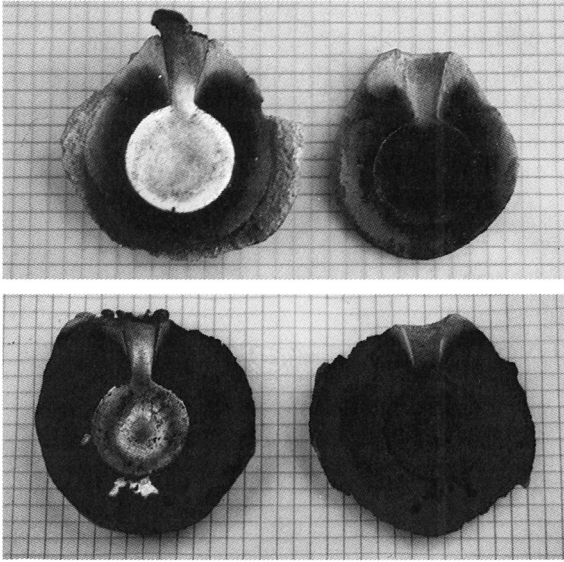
Formens reducerende indre beskytter den støbte genstands overflade mod iltning. Fig. 8 viser en genstand, hvis form først blev brudt åben efter afkøling til håndvarme. Fig. 9: Formen blev brudt før afkølingen var tilendebragt, så metallet er blevet iltet på overfladen.
